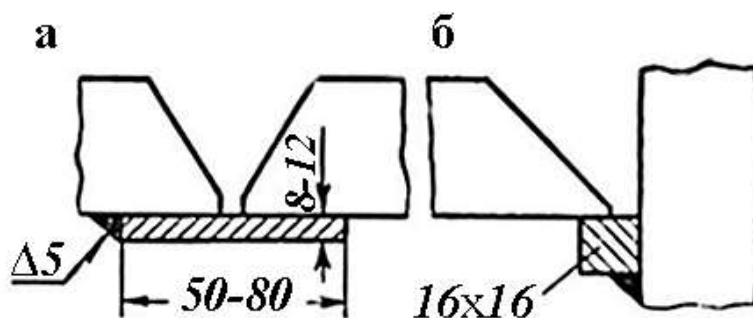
Конструкции стыковых сварных швов на подкладках
